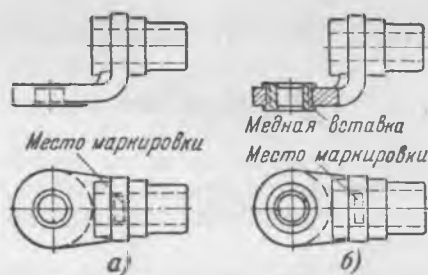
Литые алюминиевые наконечники типа ЛА в исполнении для пайки или сварки.
